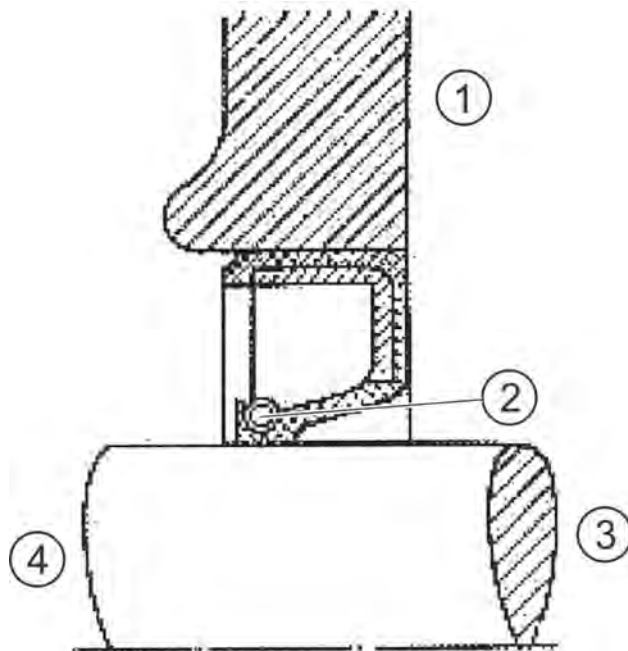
Posición de montaje de un retén radial de estanquidad para ejes rotativos sin tope limitador
